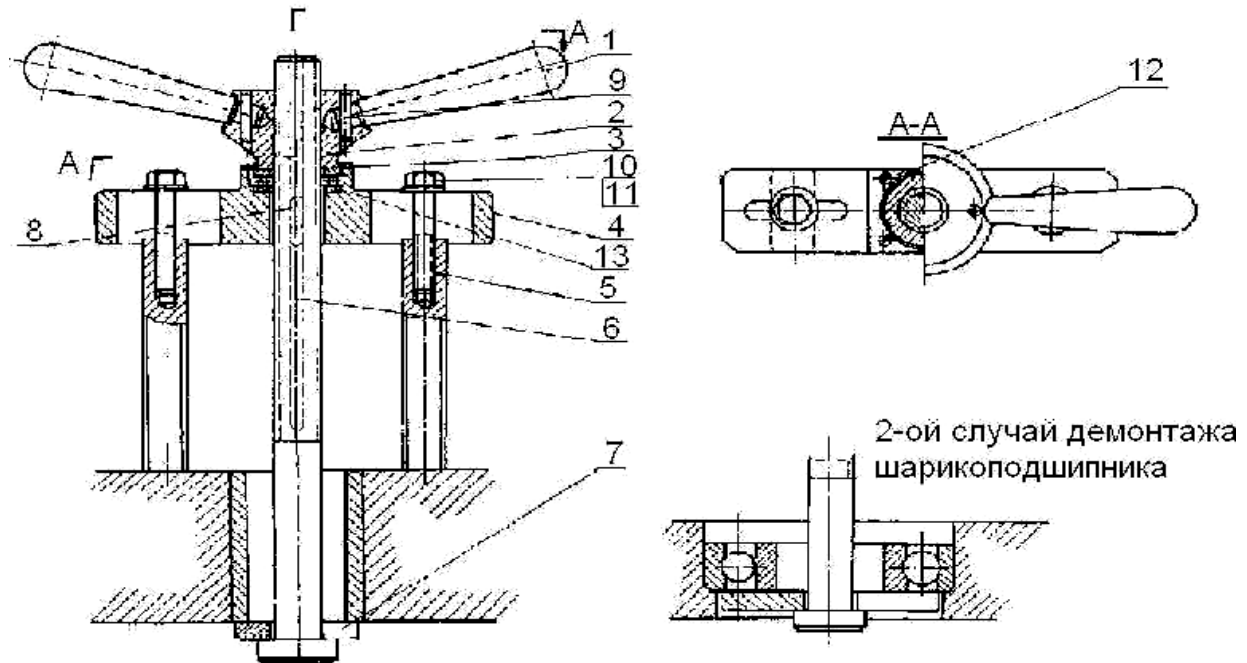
Универсальное приспособление для съёма втулок и шарикоподшипников
